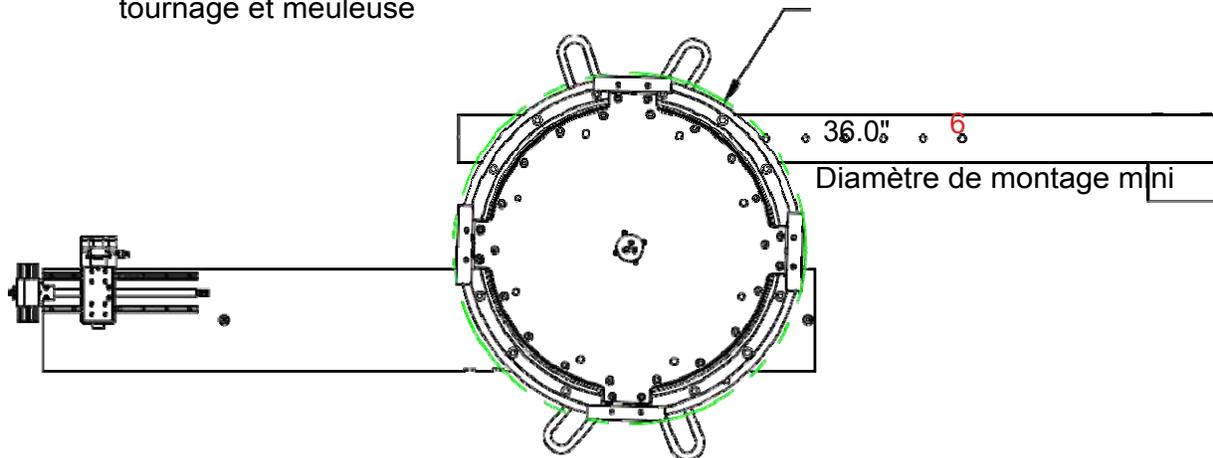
DIMENSIONS POUR MONTAGE EN SURFACE EN POINT UNIQUE
